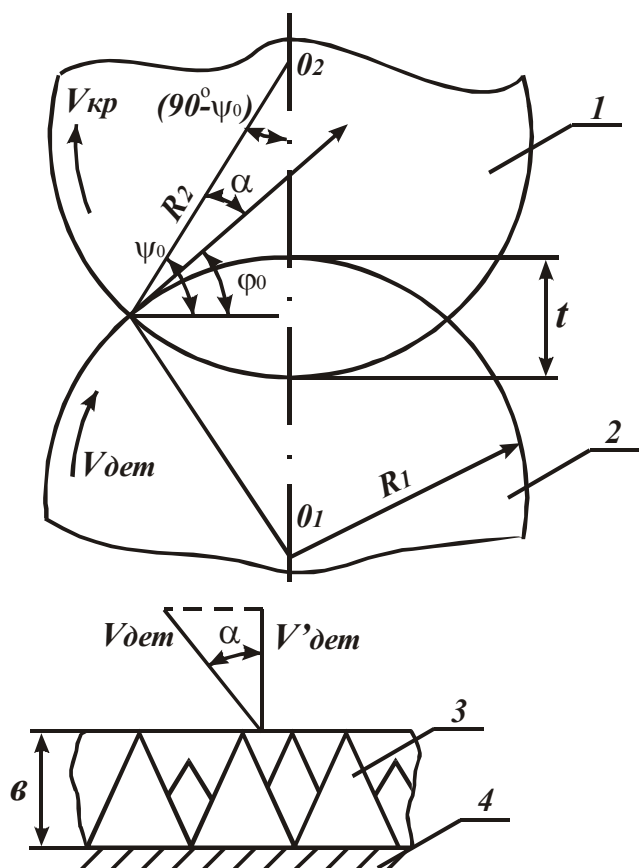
Расчетная схема круглого продольного шлифования: 1 – круг; 2 – деталь; 3 – зерна круга; 4 – связка круга.
